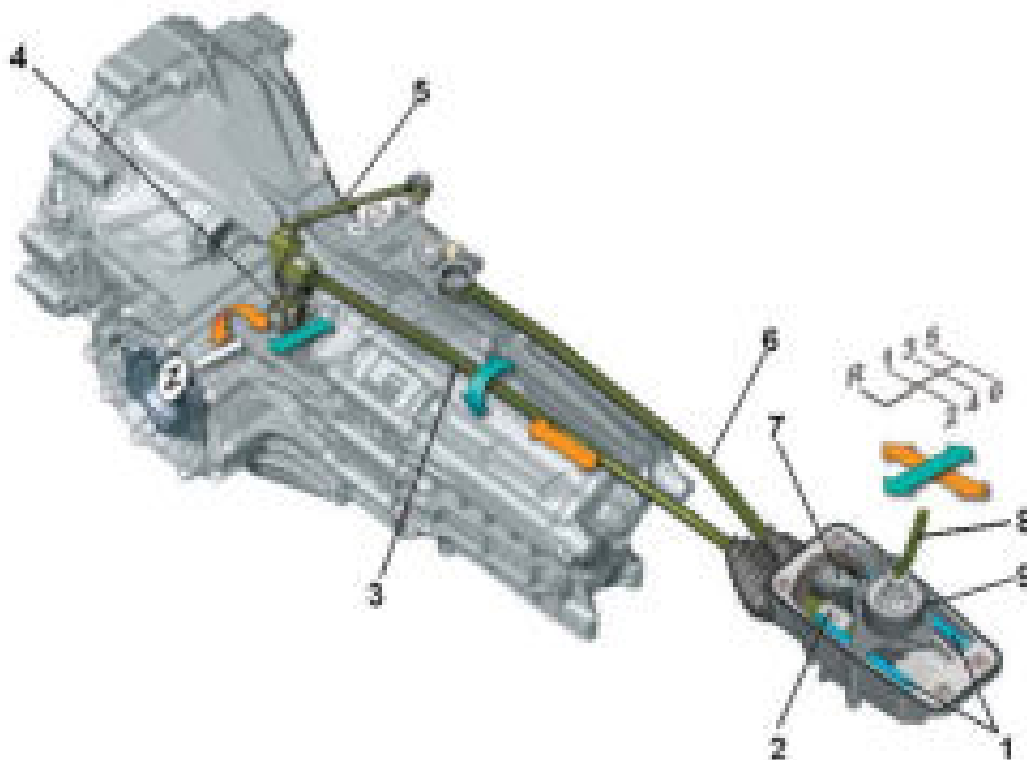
Пятиступенчатая двухвальная коробка передач переднеприводного автомобиля с поперечным расположением двигателя.
